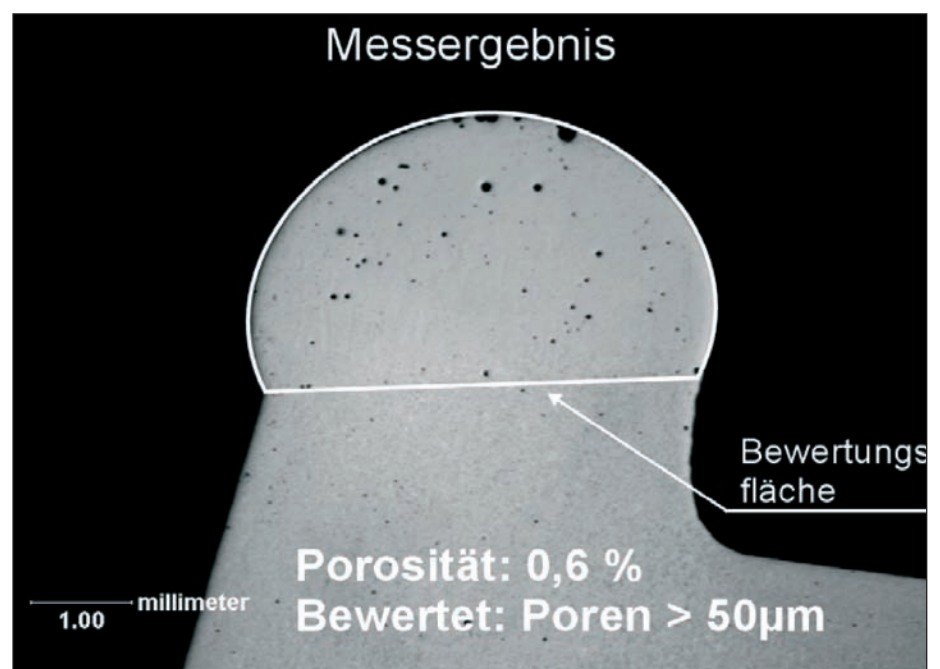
Querschliff einer Testnaht an einem schweißgeeigneten Druckgussbauteil
